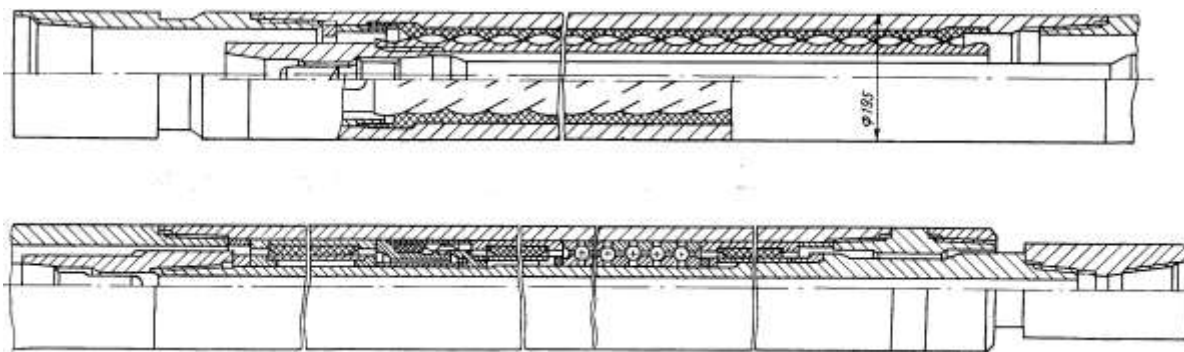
Винтовой забойный двигатель типа Д2-195 с полым ротором.
